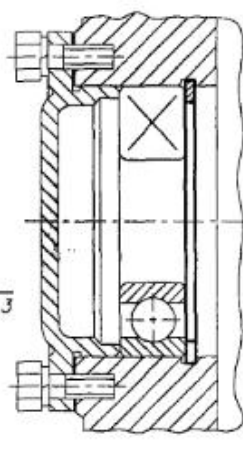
Закрепление наружного кольца подшипника качения в корпусе с использованием пружинного кольца
